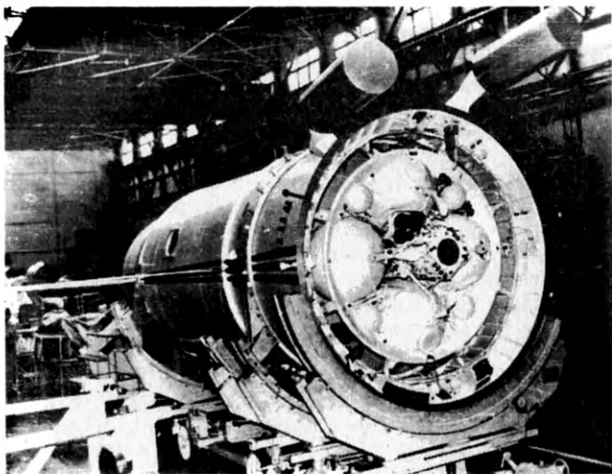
Внешний вид макета корабля 7К-ВМ ЦСКБ-Прогресс.
